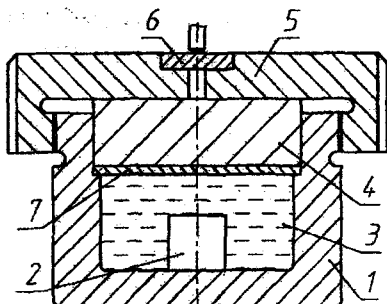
Штамповка взрывом с использованием воды в качестве передающей среды: 1 – корпус; 2 – заготовка; 3 – вода; 4 – БВВ; 5 – крышка, навинченная на резьбу; 6 – капсюль; 7 – мембрана, разделяющая воду и БВВ
